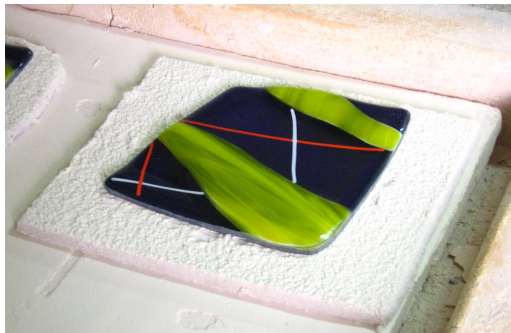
Aspecto de la pieza terminada el proceso de fusión
